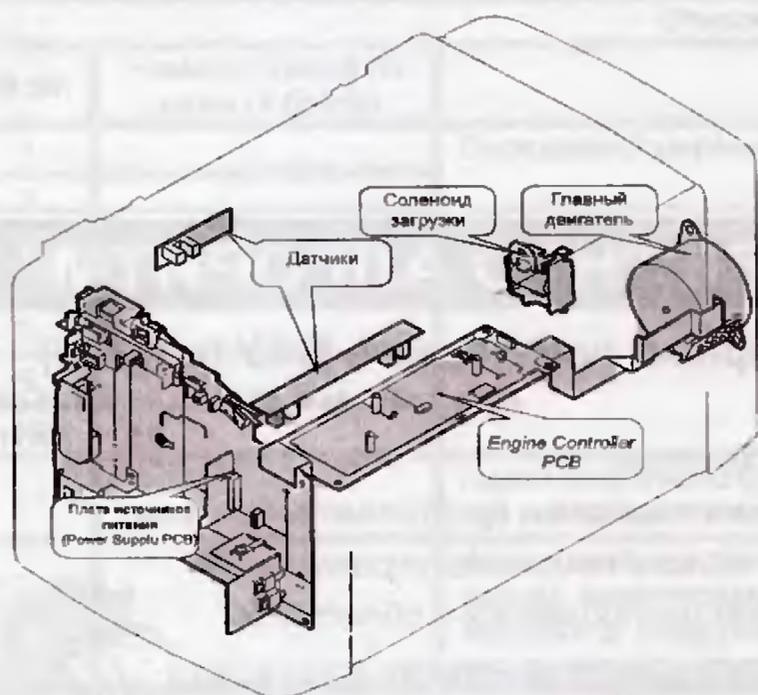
Расположение в принтере МФУ HP LJ3050 платы источников питания (Power Supply PCB) и платы контроллера механизмов (Engine Controller PCB)
